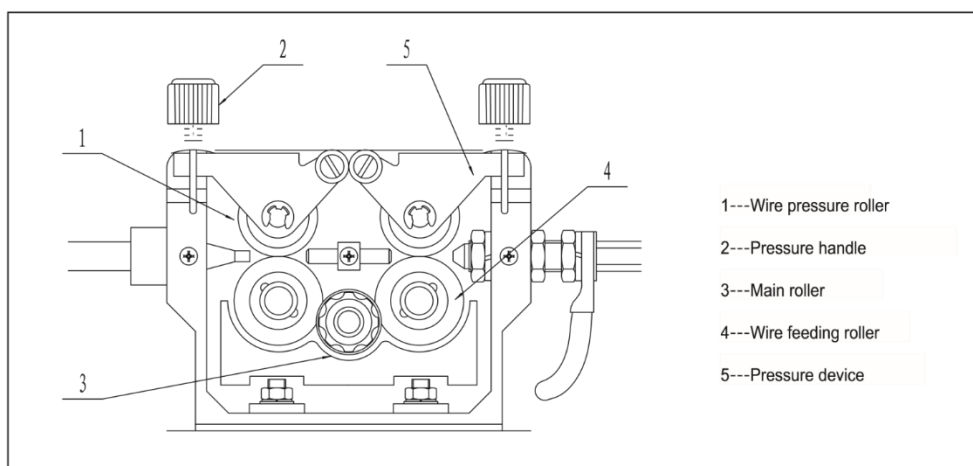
Привод закрытого механизма подачи проволоки
